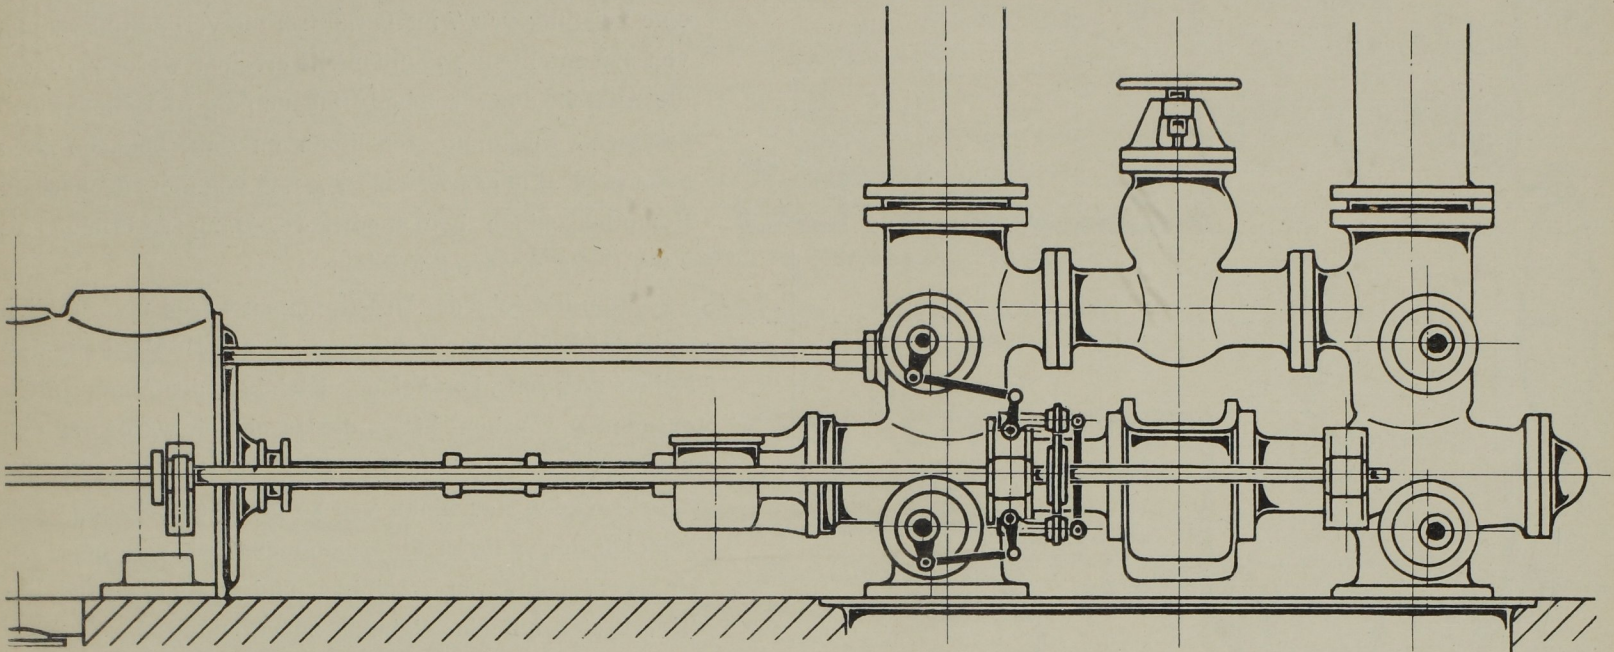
Seitenansicht der Druckpumpe. Masst. 1:30.
